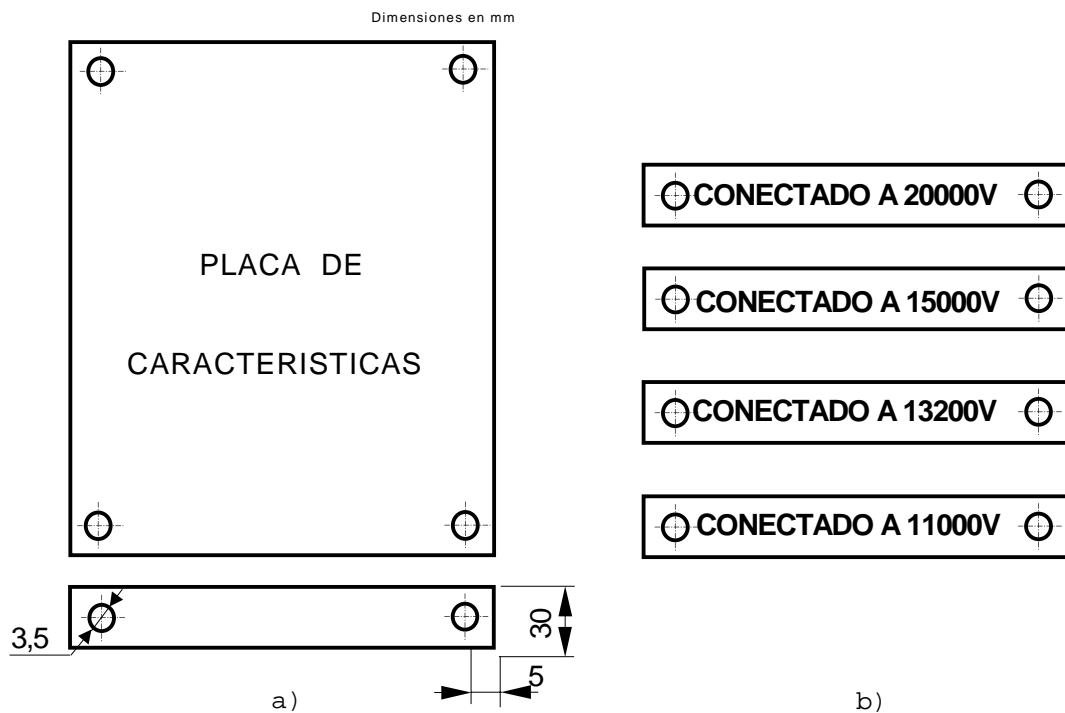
Dimensiones, disposición y texto de la placa indicadora de conexión
